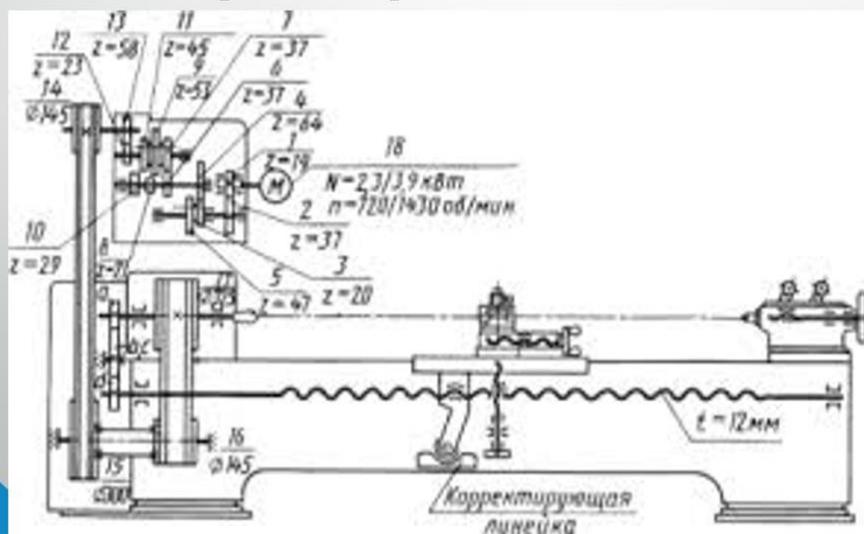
Кинематическая схема коробки скоростей токарного станка со шкивом плоскоремённой передачи.
